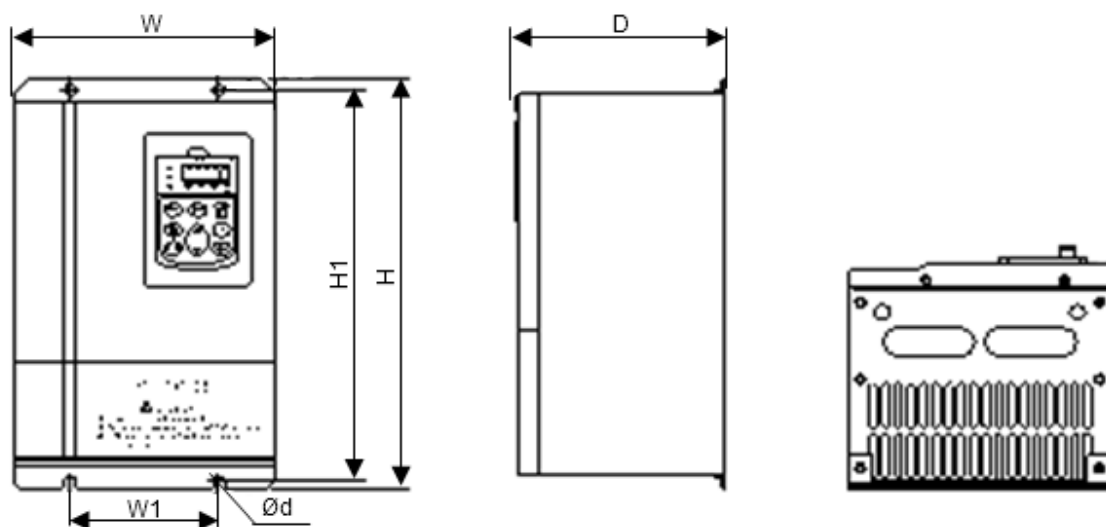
Внешний вид инвертора SL9 в металлическом корпусе
